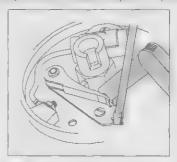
38 Регулировка контактов прерывателя с пазовой регулировкой
